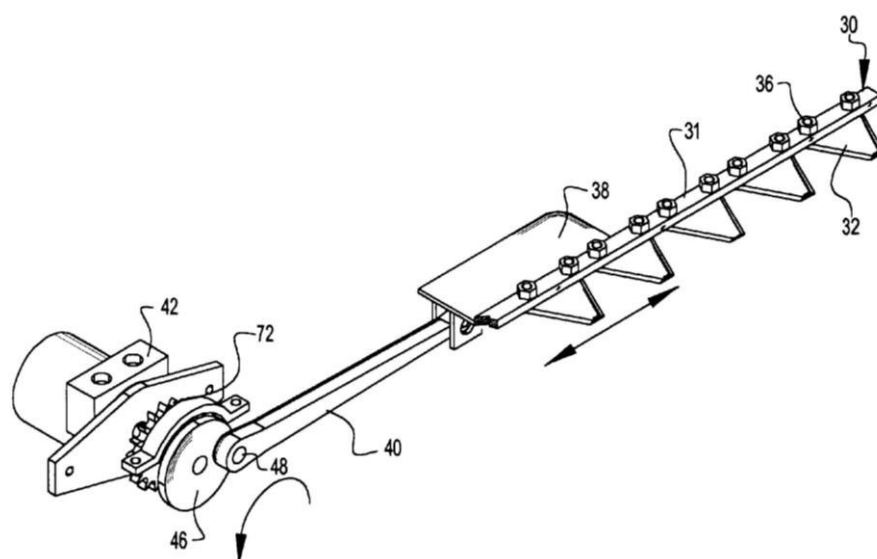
Механізм зворотно-поступального руху жатки
